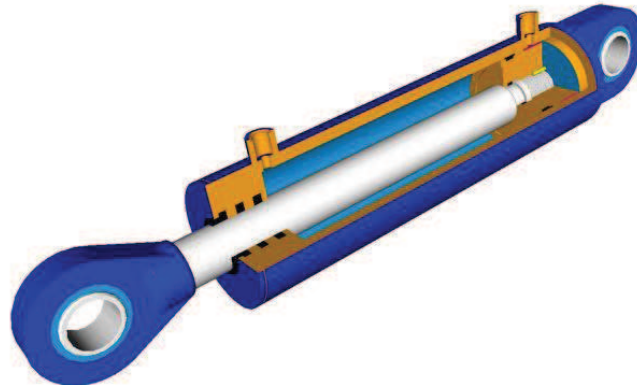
Kyvný hydromotor s přímočarým hydromotorem [6]
